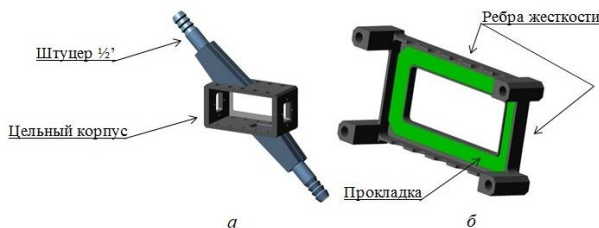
Элементы корпуса и предусилителя: а – сварной корпус, б – крышка с прокладкой
